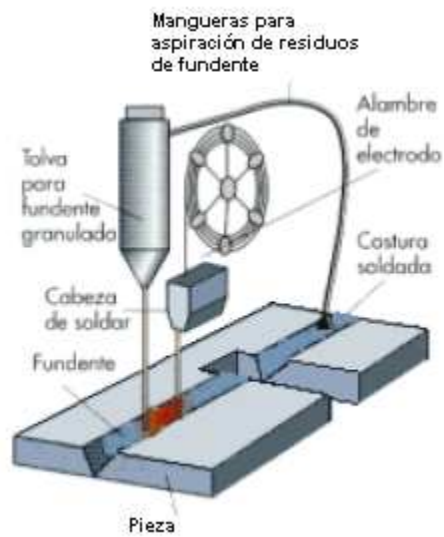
Equipo necesario para soldadura por arco sumergido
